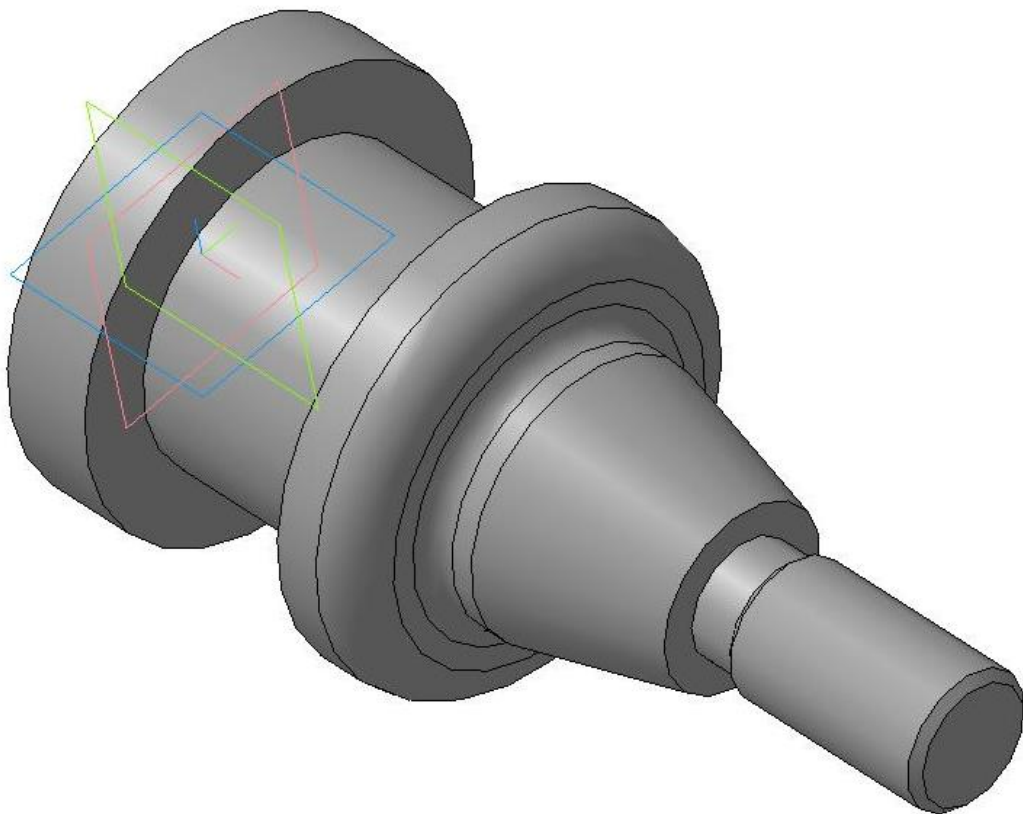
Загальний вигляд деталі «Втулка»
